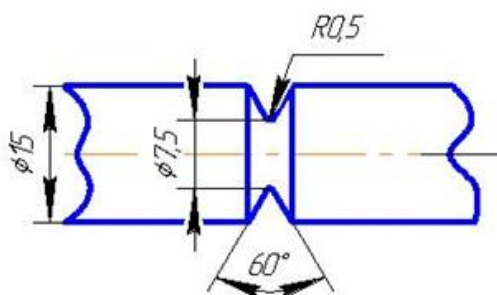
Рабочая часть образцов с V-образным надрезом из сталей ВНС40 и 38Х2МЮА
